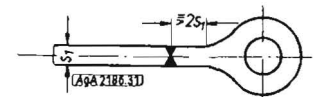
Einfache Form eines Gelenkauges, doch ist diese Form nur für Schmelzschweißung zu empfehlen. Bei sorgfältiger Ausführung ist sie auch für größere Kräfte ausreichend
